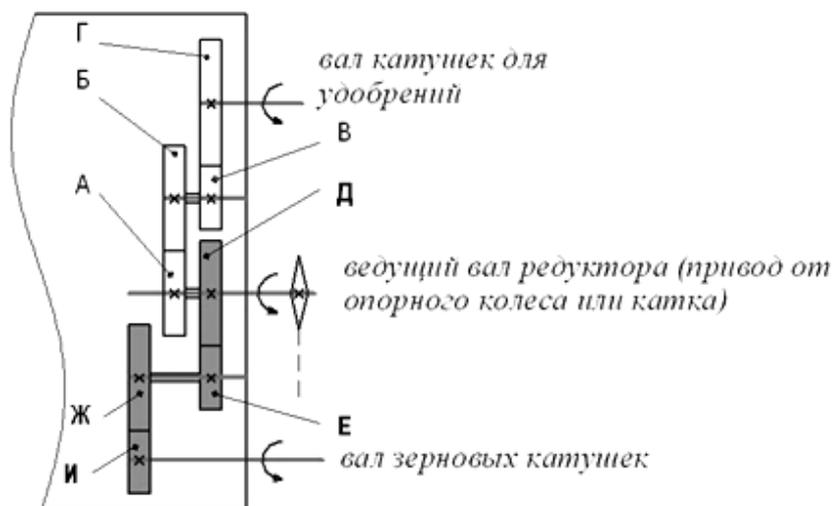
Схема редуктора сеялки СЗ-3,6
